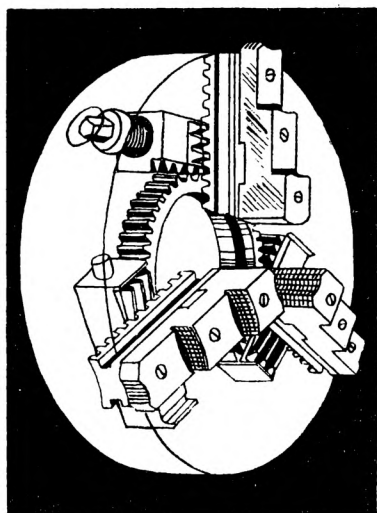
Винтовой патрон с червячной и конической передачей.
